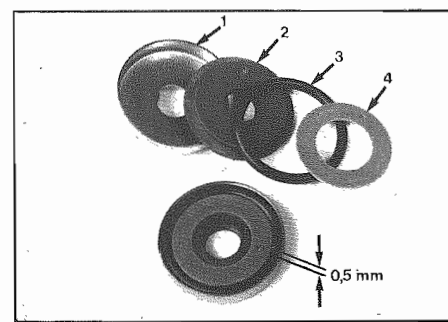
1 - Coperchio parapolvere - Dust cap
